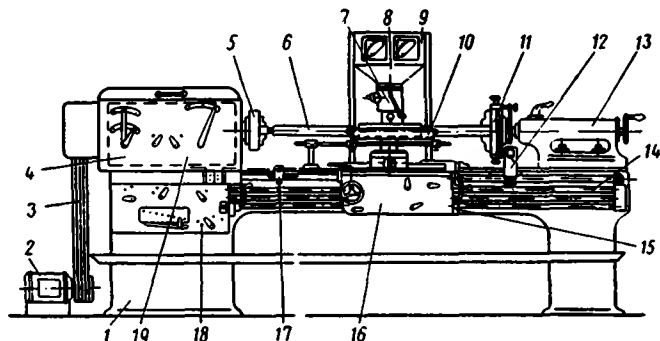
Универсальная полуавтоматическая установка для восстановления деталей вибродуговой наплавкой под слоем флюса:
